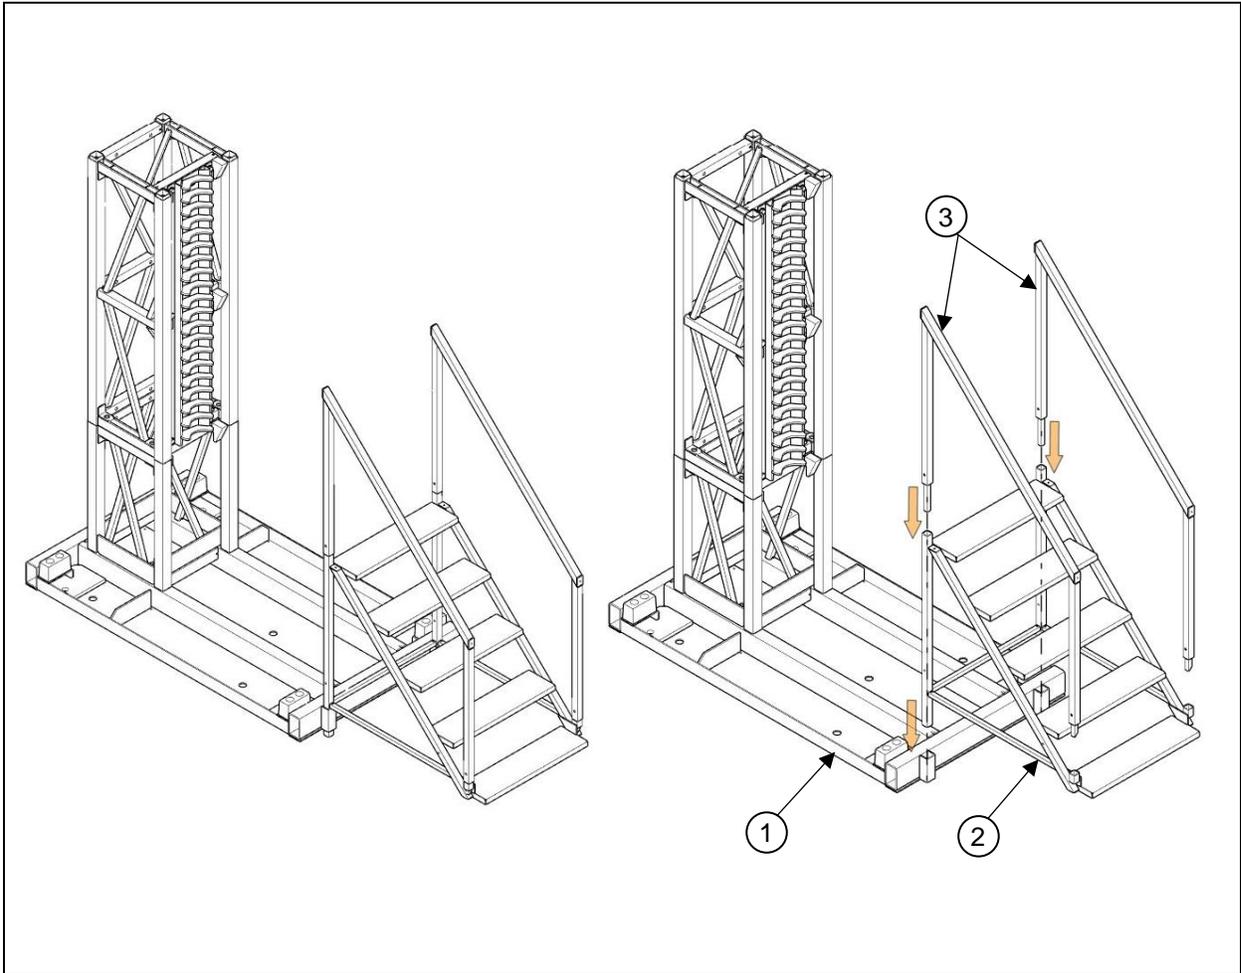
Installation de l'escalier 5 marches sur base au sol
